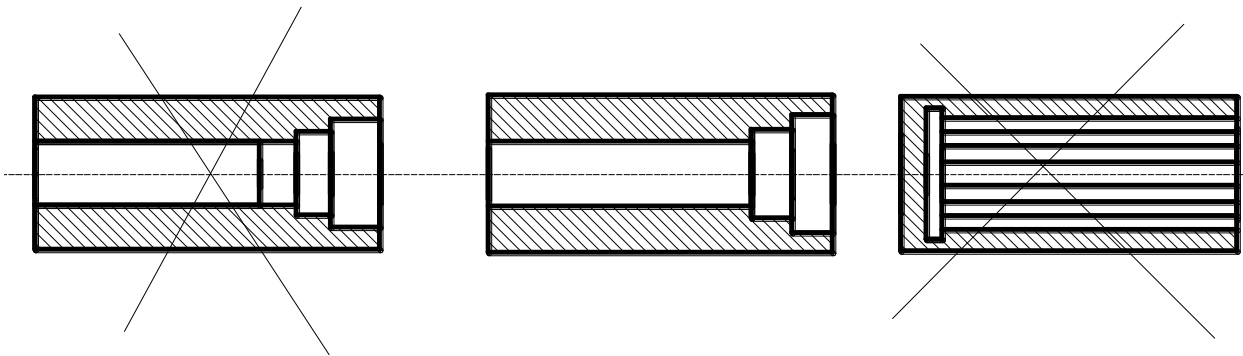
Базування втулок по чорнових базах (в самоцентруючому патроні або цанзі) на токарно-револьверному верстаті
